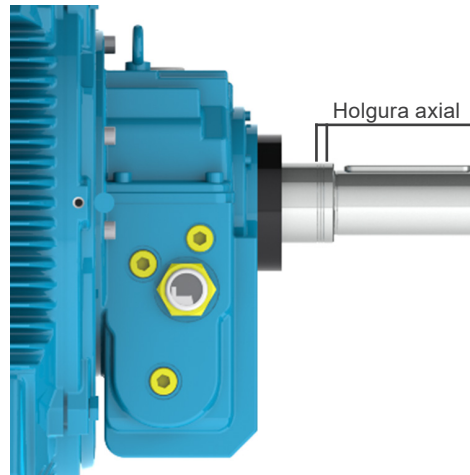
Holgura axial en motor equipado con cojinete de deslizamiento
